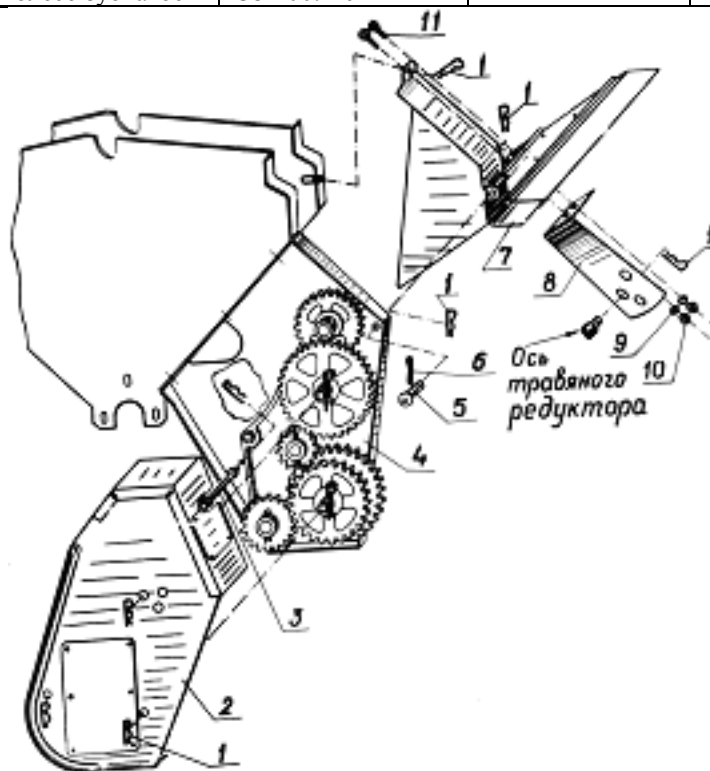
Крепление щитков редуктора СЗГ 00.070
